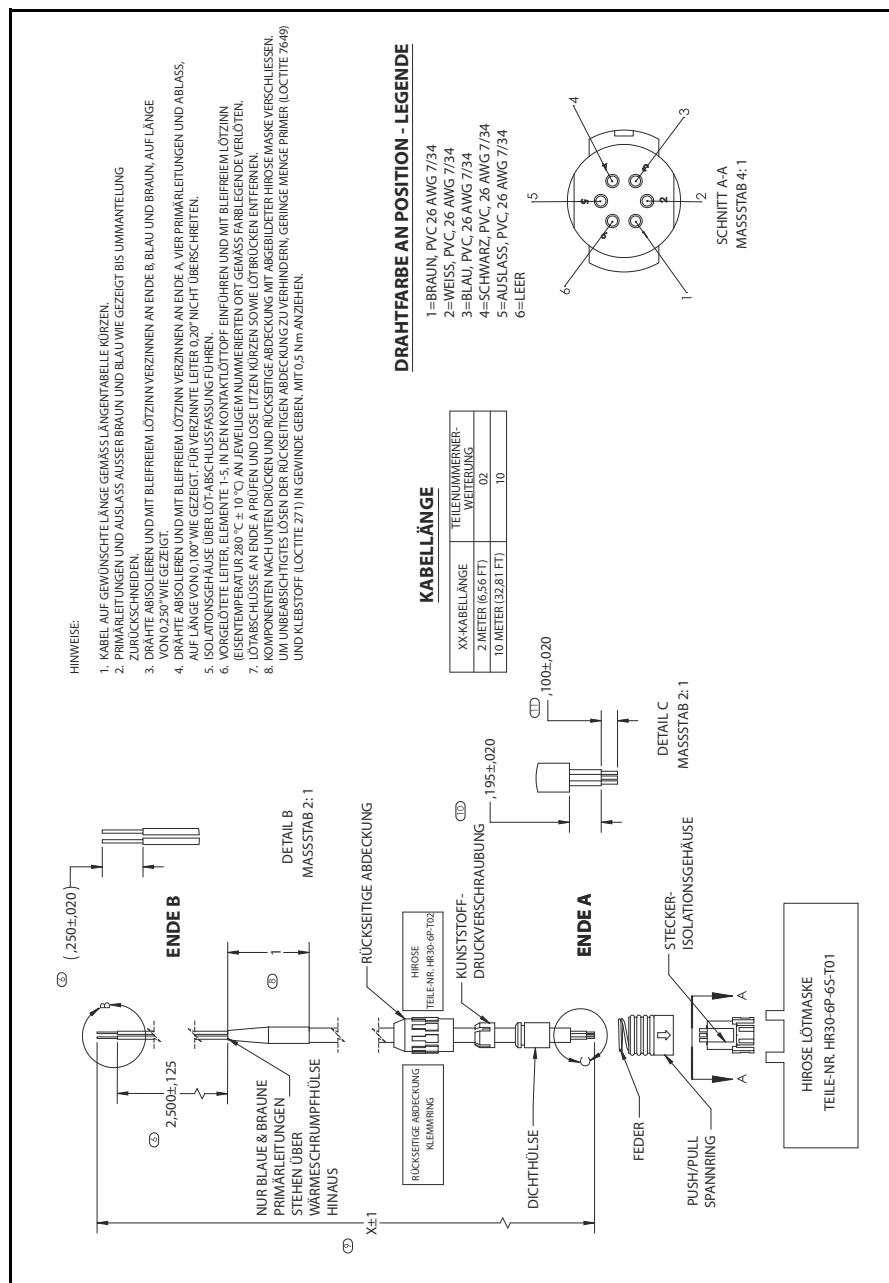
Kabel, Standard (siehe Zeichnung 704-1317, Blatt 2 von 2)
